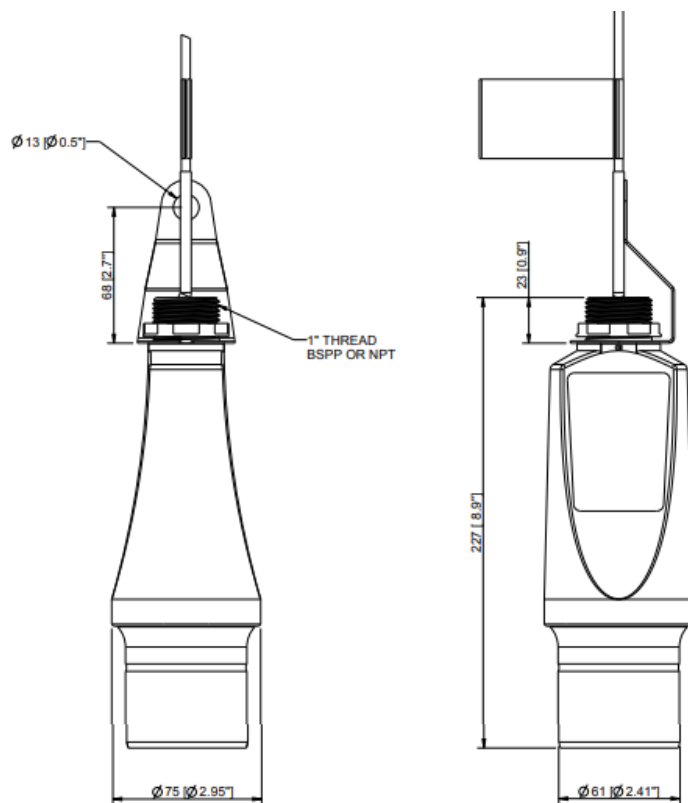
Габаритные и установочные размеры Rosemount 3100
